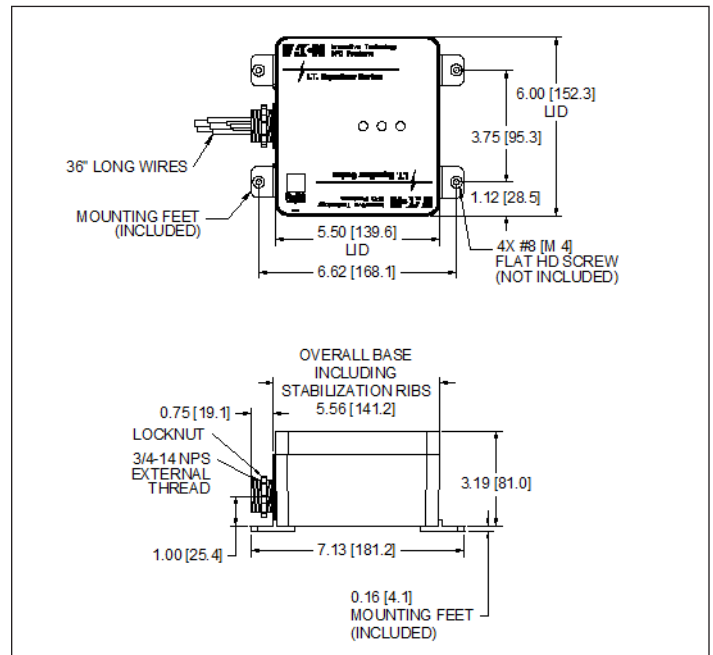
Dimensiones de la caja P1 con patas de montaje.
